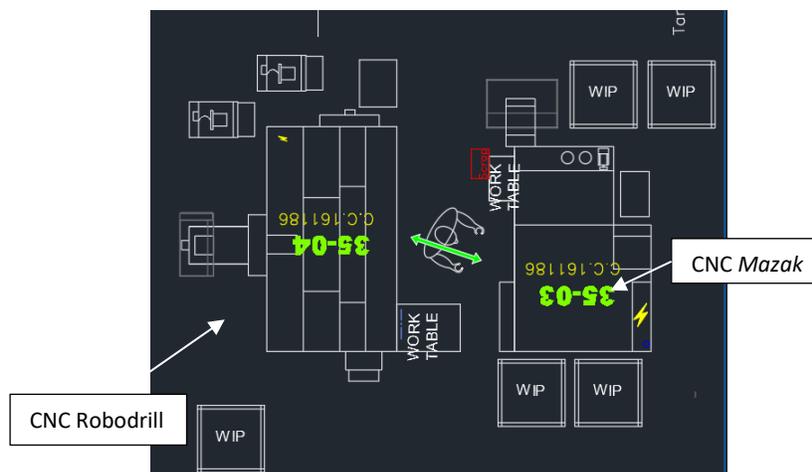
Layout de estación de Trabajo de maquinado CNC. Fuente: Elaboración propia
